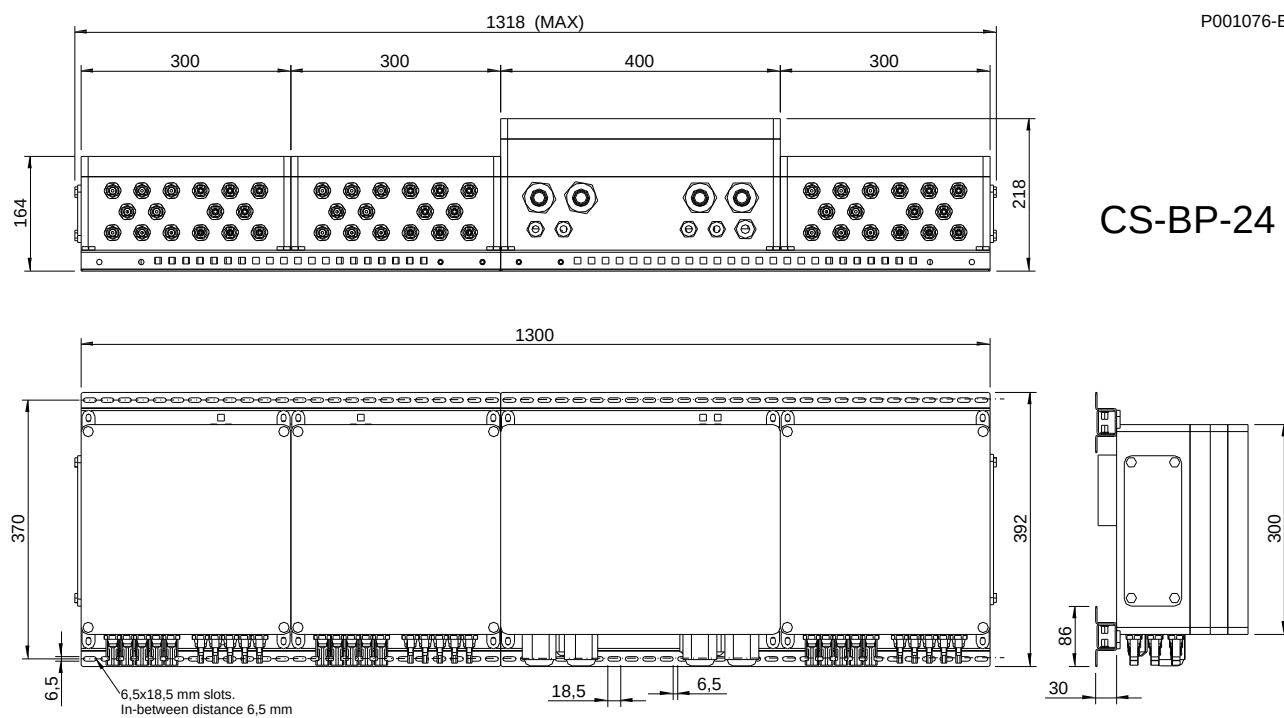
Размеры коммуникатора STRING BOX CS-BP-24.
